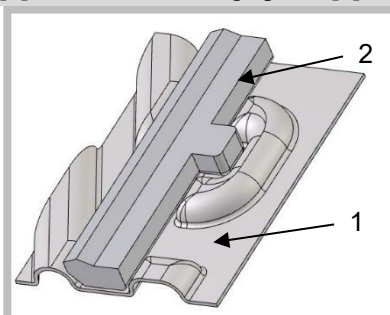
Ausschnitt Wärmeübertragerplatte [1] mit eingesetzter Dichtung [2]
